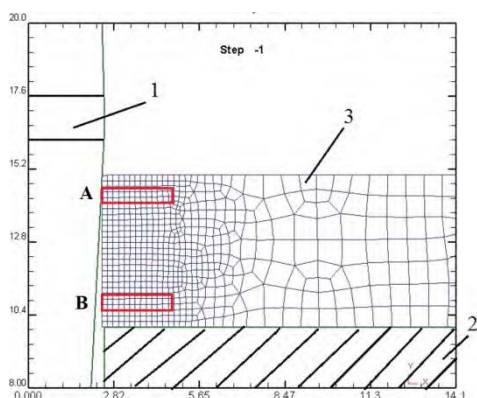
Конечно-элементная модель процесса дорнования (1 – дорн, 2 – матрица, 3 – заготовка с КЭ сеткой)
